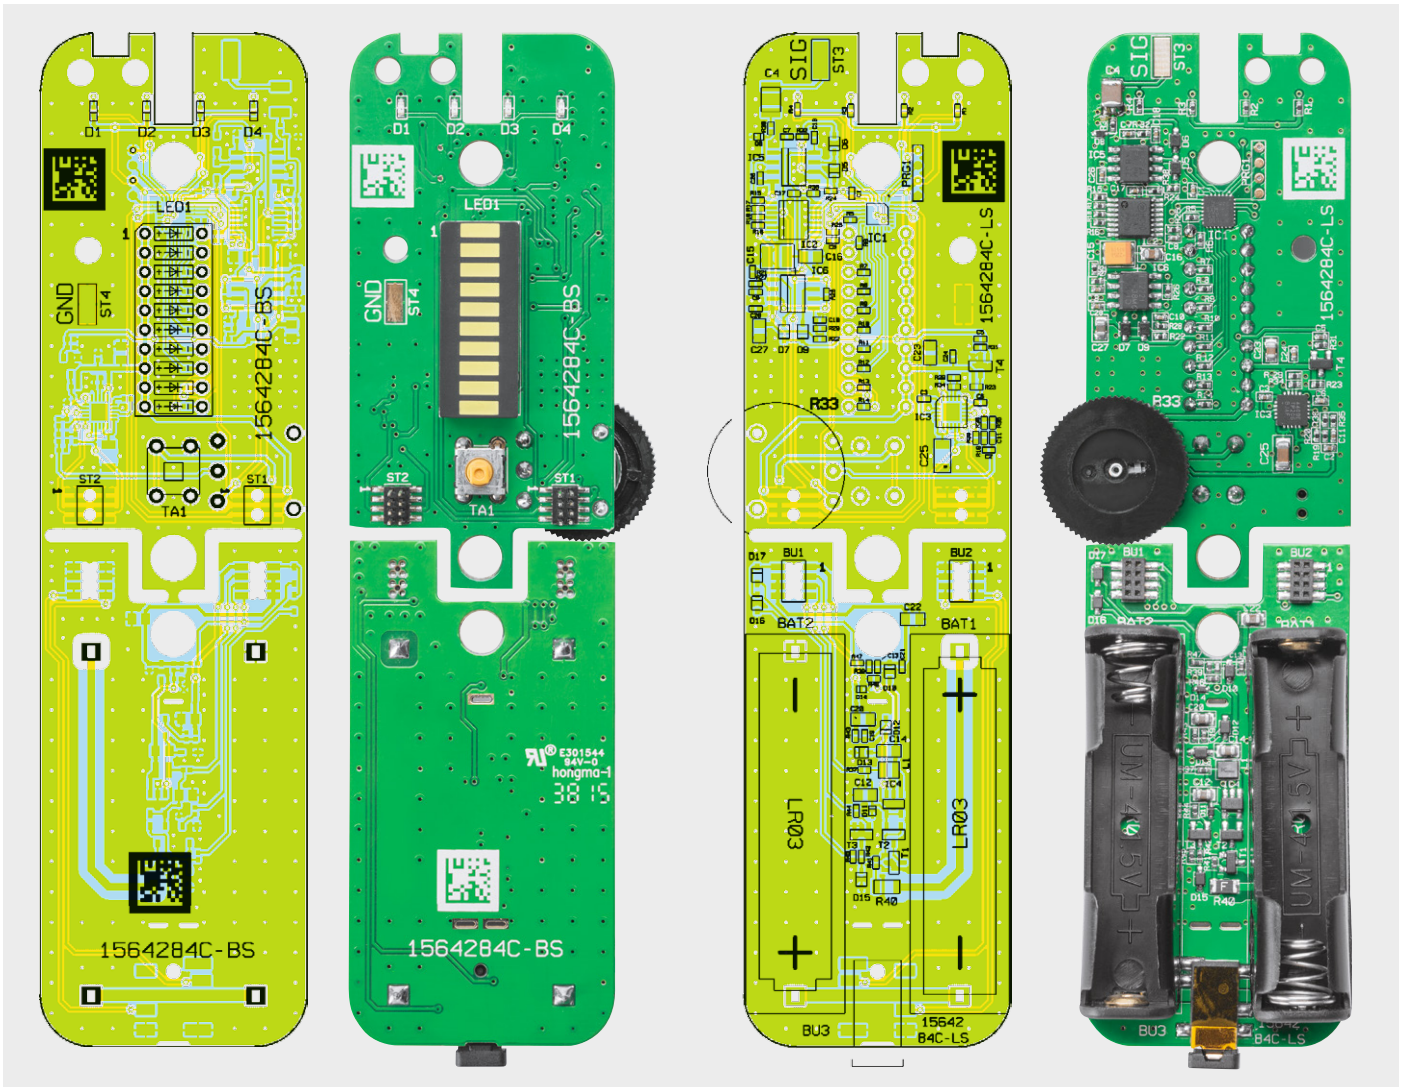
Platinenfotos der komplett bestückten Teilplatinen mit den zugehörigen Bestückungsplänen
